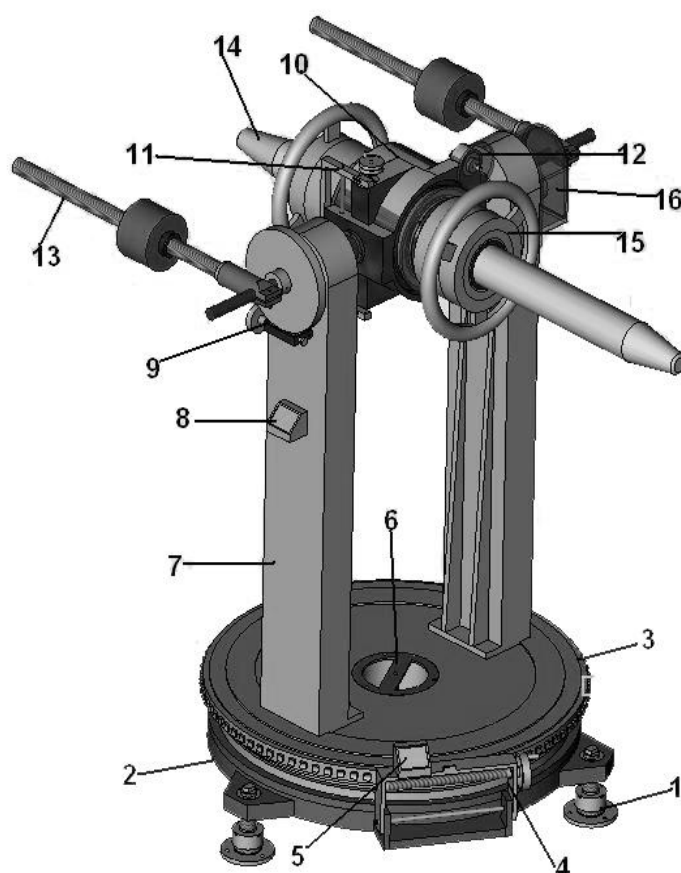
Общий вид установки для поверки магнитных инклинометров: 1 – регулируемая опора; 2 – основание; 3 – опорно-поворотный узел; 4 – ручной привод азимутальной оси; 5 – цифровой индикатор азимутального угла; 6 – датчик положения азимутальной оси; 7 – стойка; 8 – цифровой индикатор зенитного и апсидального углов; 9 – ручной привод зенитной оси; 10 – зенитная поворотная рама; 11 – привод зенитной оси; 12 – датчик положения апсидальной оси; 13 – балансирующее устройство; 14 – поверяемый инклинометр; 15 – цанговый зажим; 16 – датчик положения зенитной оси
